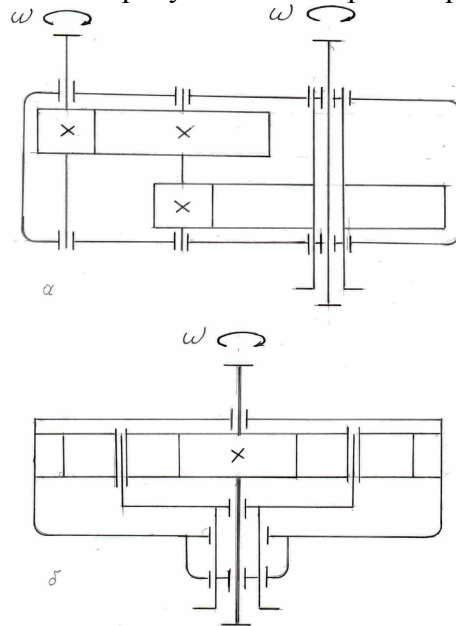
Схема обертальників з співвісними вихідними валами: а – з двома вхідними валами; б – з планетарним механізмом
